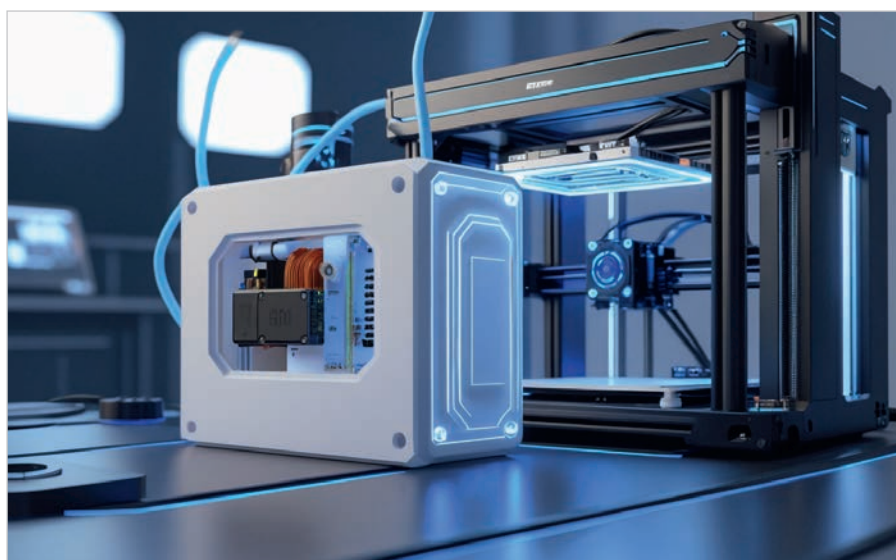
3D-принтер для пластиковых корпусов РЭА
